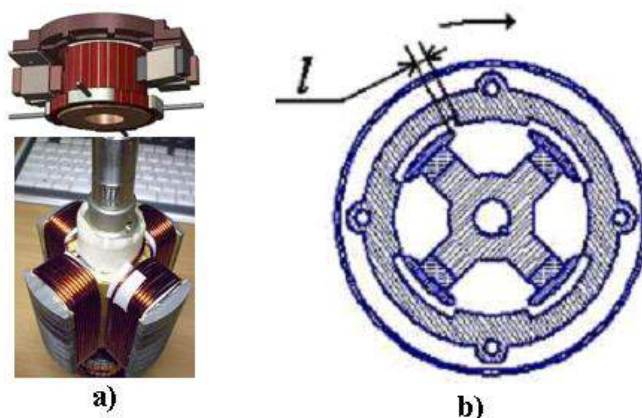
а) ротор МГ-2; б) схема разреза ротора и статора МГ-2
